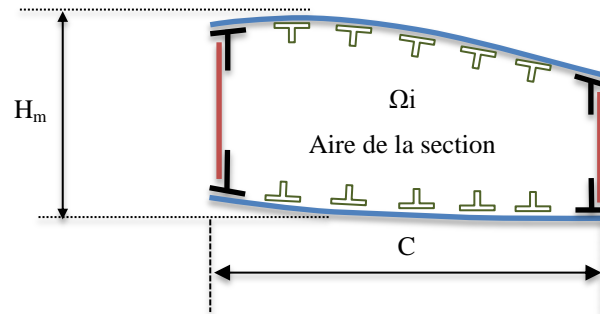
Aire d'une section du caisson d'aile à la station i
